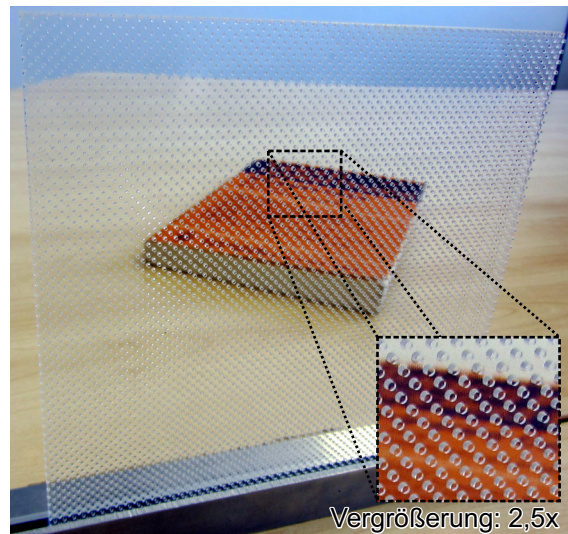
Durch Heißprägen von *Jungbecker* gefertigter Prototyp mit einer Kantenlänge von 155 mm. Der vergrößerte Ausschnitt zeigt die Zylinder mit einem Durchmesser von 982 μm , welche von Nahem deutlich zu erkennen sind.
